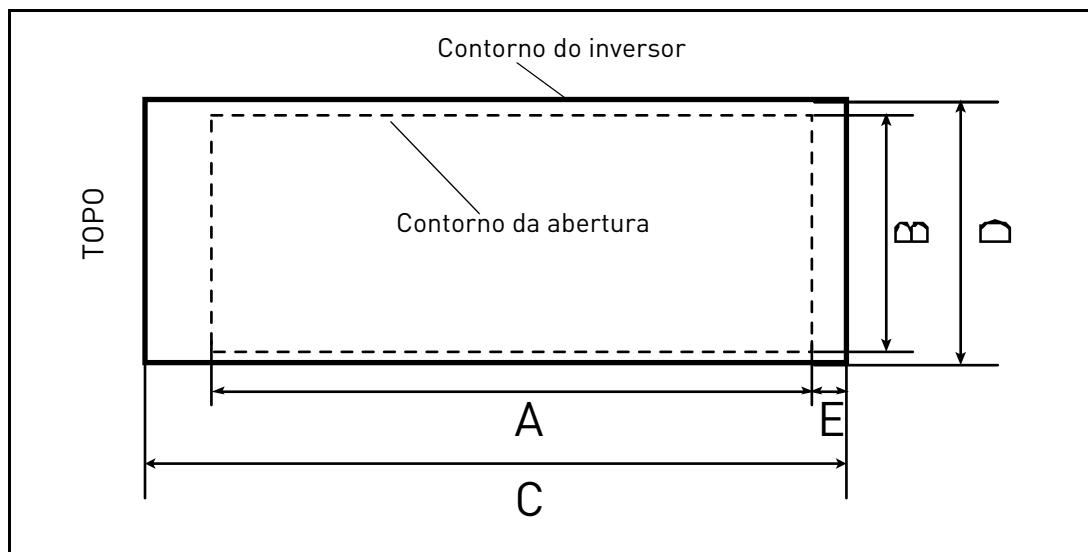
Dimensões do recorte para montagem com flange do MR7 ao MR9
